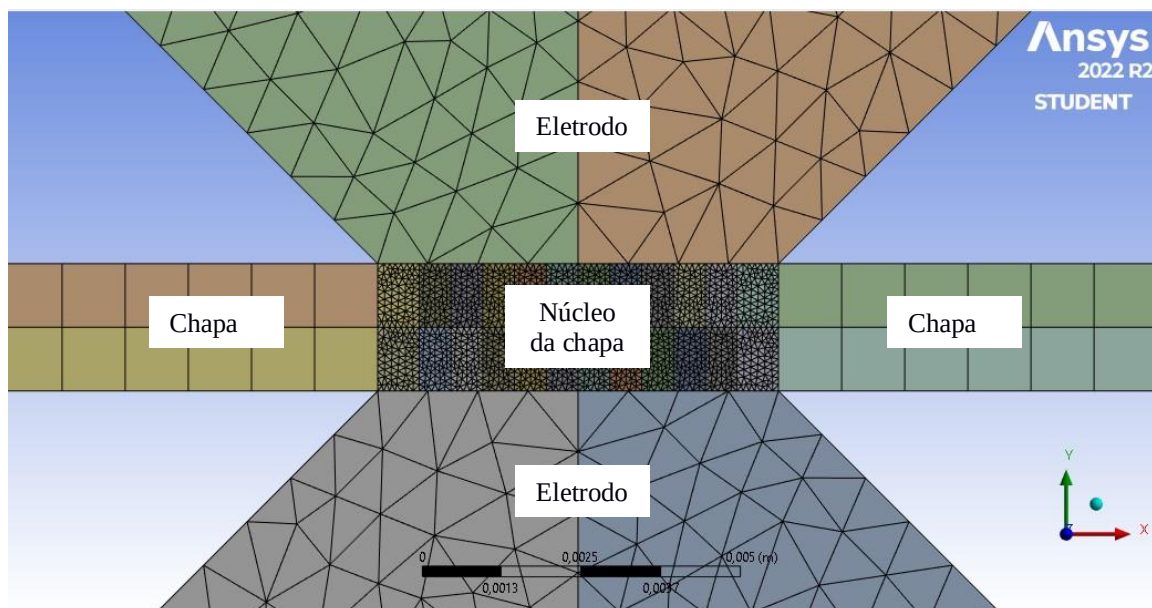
Malha vista em corte de seção transversal do modelo. (Autoria própria)
